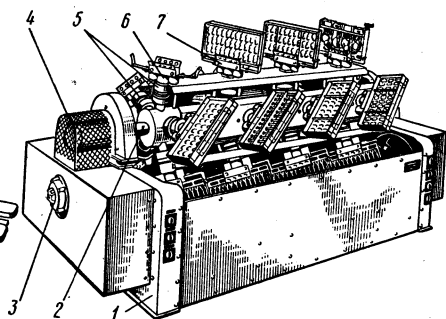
Ротационная машина модели Н для формования пустотелых шоколадных фигур центробежным способом: 1 — станина; 2 — центральный вал; 3 — электродвигатель; 4 — привод; 5 — патроны-держатели форм; 6 — магнитные фиксаторы форм; 7 — зажимы
